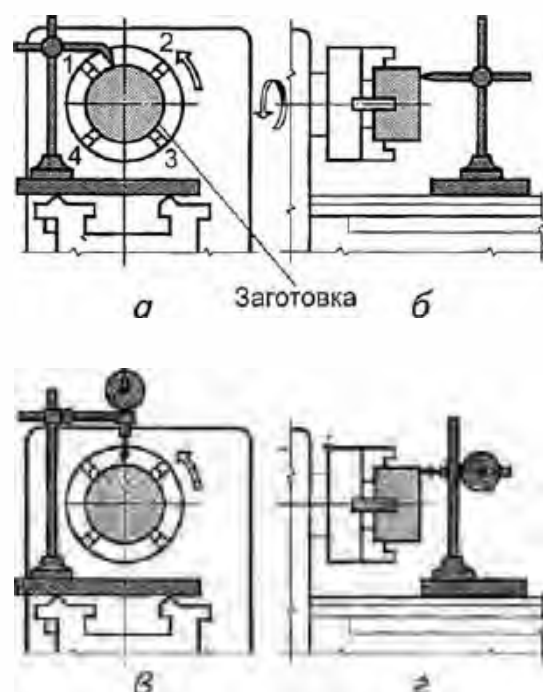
вивірення заготовки у чотири-КУЛАЧКОВОМУ ПАТРОНІ.
